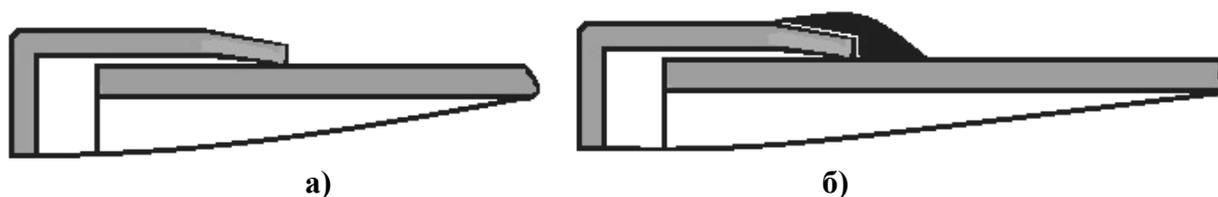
Форма шва на стыке оголовника и корпуса стационарной МСР.
